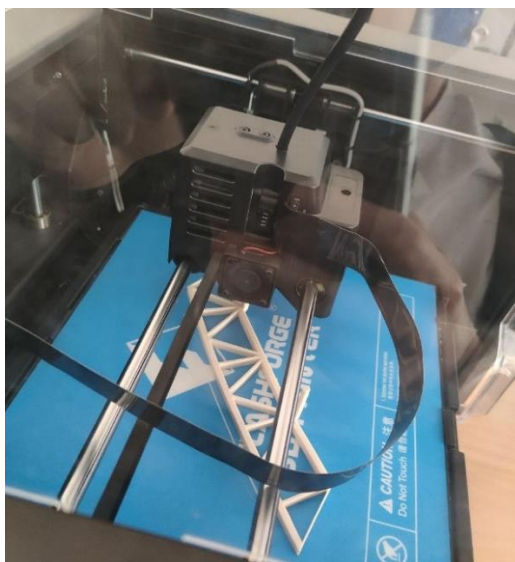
Процесс печати элемента конструкции макета теплицы
